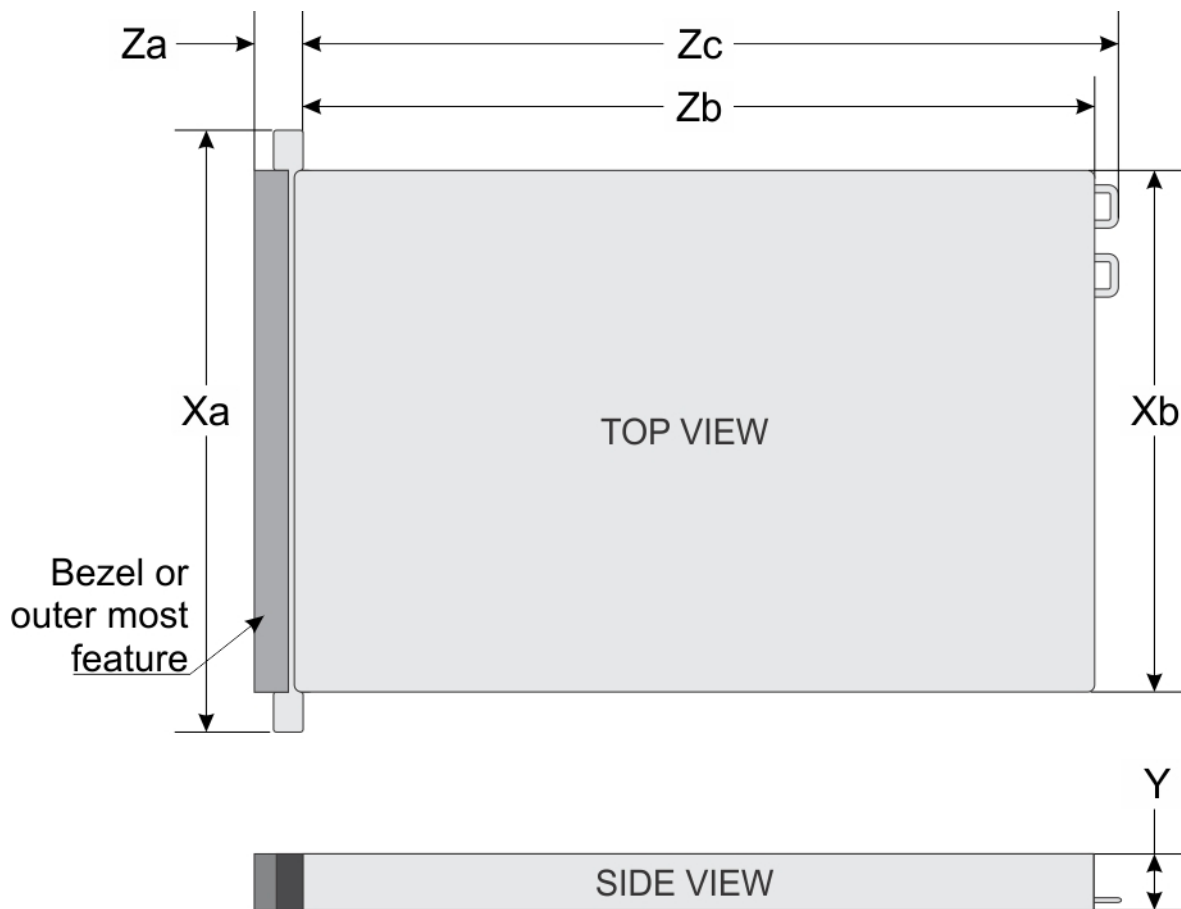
Gehäuseabmessungen des PowerEdge R450-Systems
